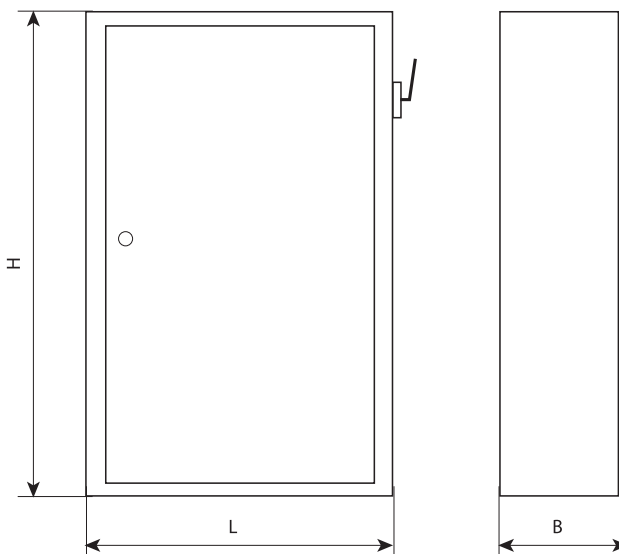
Общий вид и габаритные размеры ЯРП (В).
